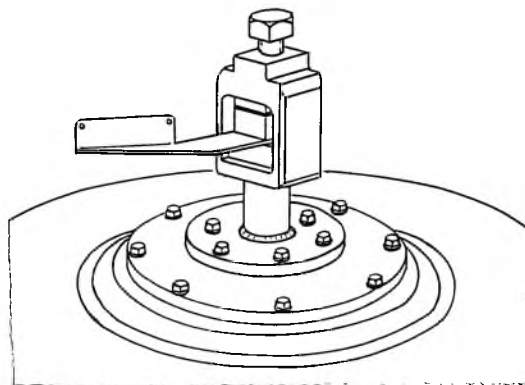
Общий вид крепления натурной детали № 1 (рис. 2,а) на подвижном столе вибратора.
